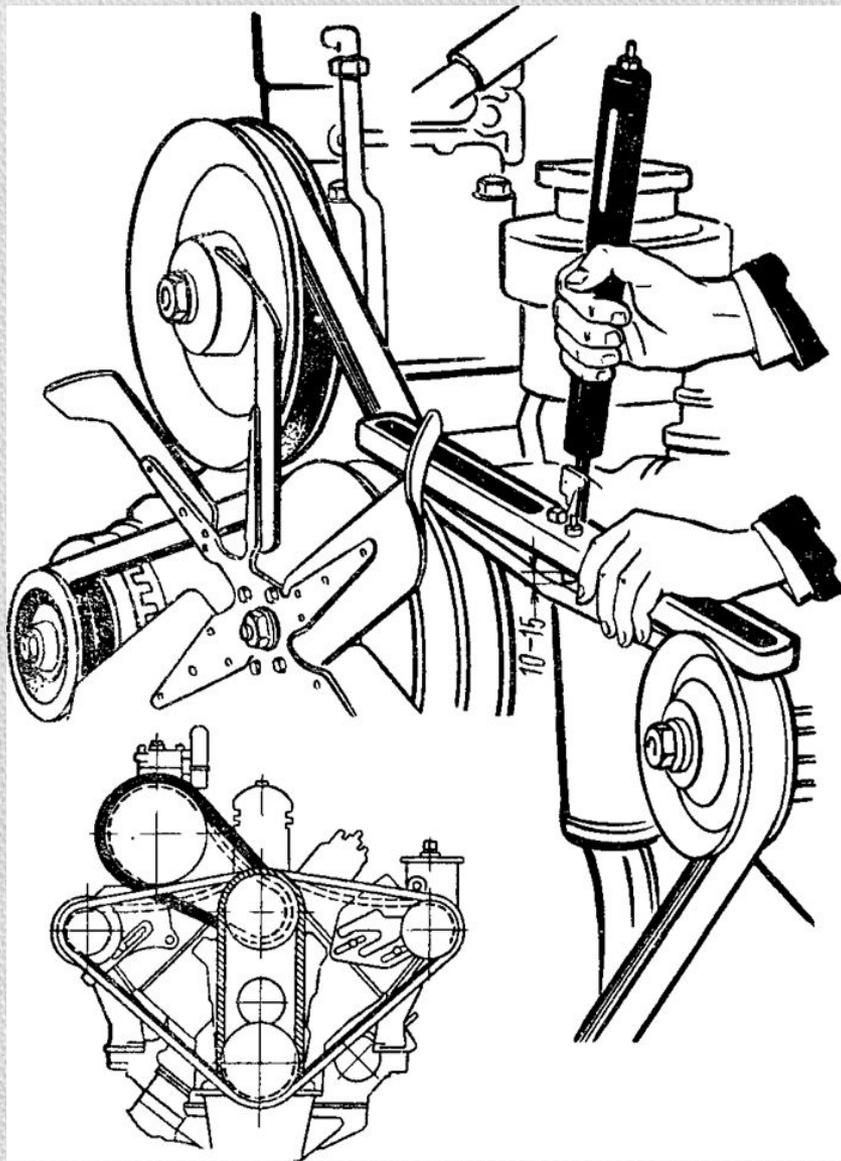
Приспособление КИ-8920 для проверки натяжения ремней: а — проверка натяжения, б — прибор для проверки натяжения
